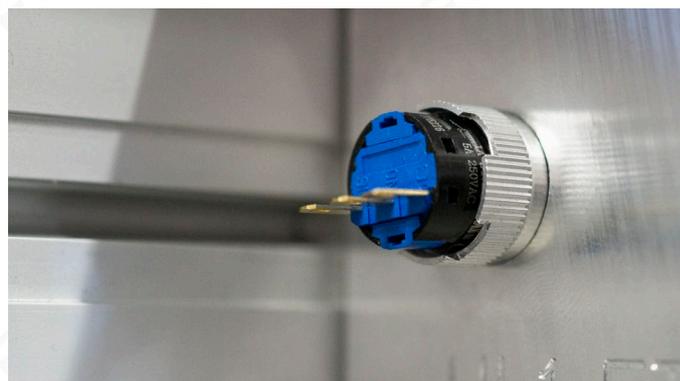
Montage des Notaus-Schalters, Sicht von hinten
